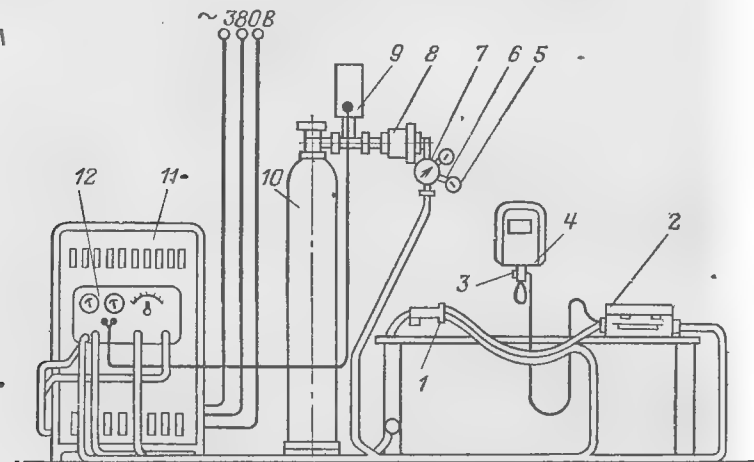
Схема поста А-547Р для полуавтоматической сварки в среде углекислого газа.
